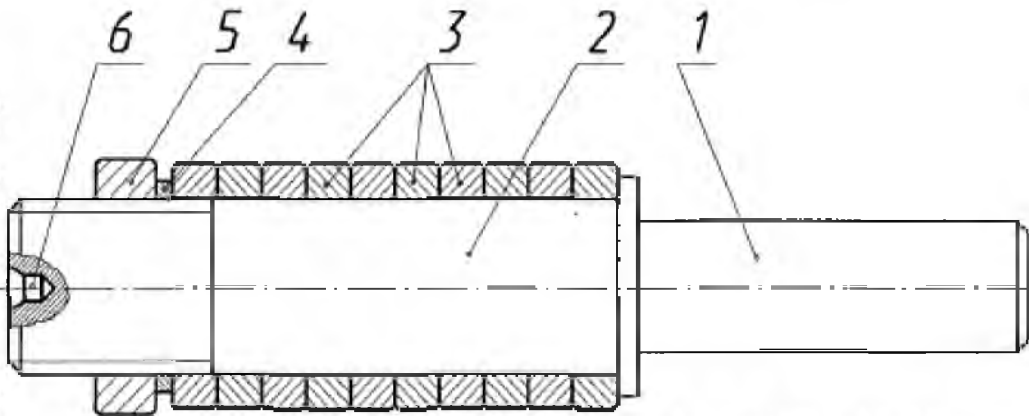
Пристрій для підготовки зовнішнього діаметра сідел клапанів під міднення: 1 - вал пристрою; 2 - лідер; 3 - сідла клапанів; 4 - шайба; 5 - гайка; 6 - центруючий отвір.
